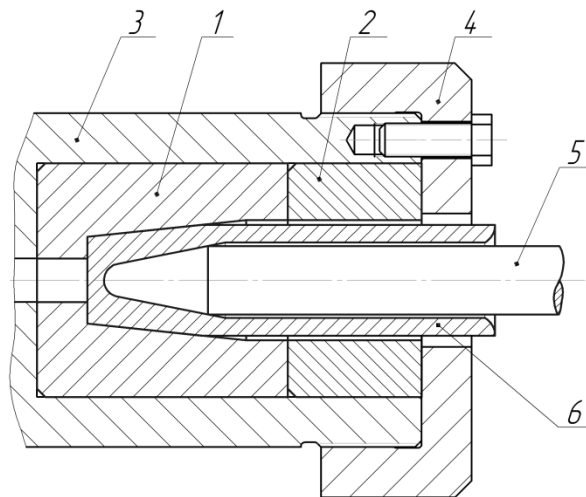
Технологический инструмент для калибрования донной части полых заготовок:
